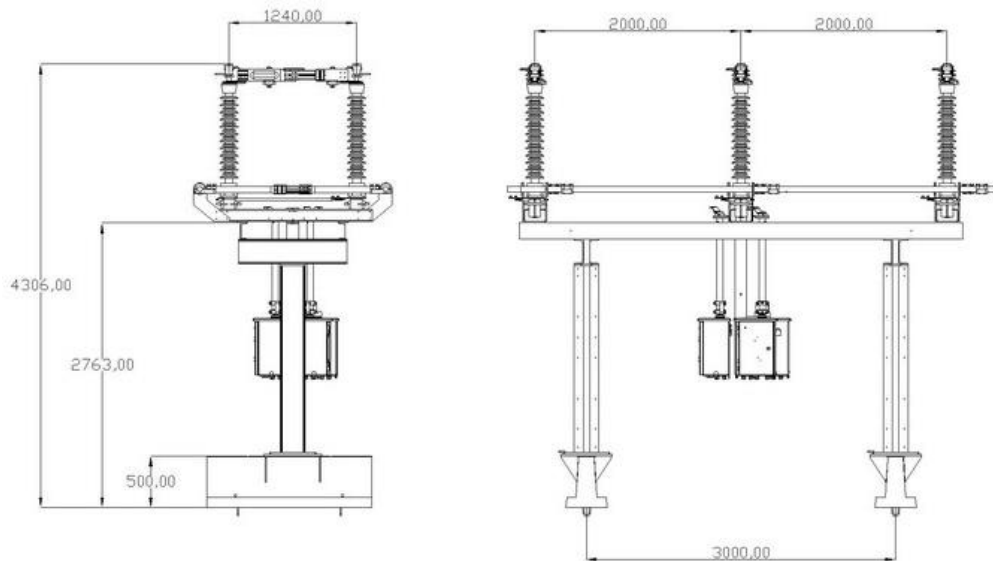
Конструктивный вид разъединителя РГП2–110/1000УХЛ1
